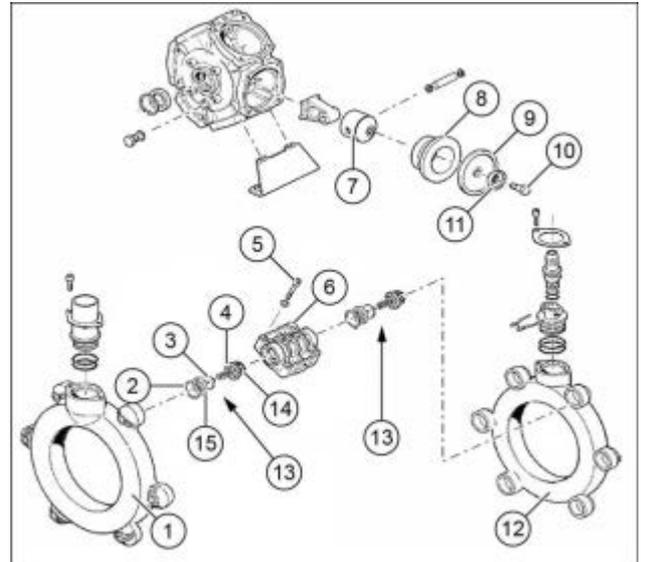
Explosionsdarstellung Spritzmittelpumpe
